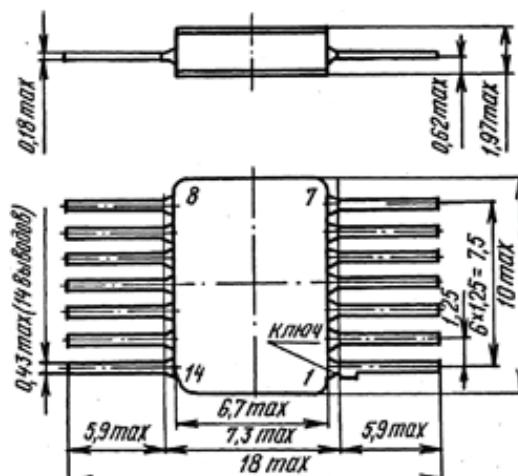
Габаритные чертежи корпусов 401.14-4 и 401.14-5М
